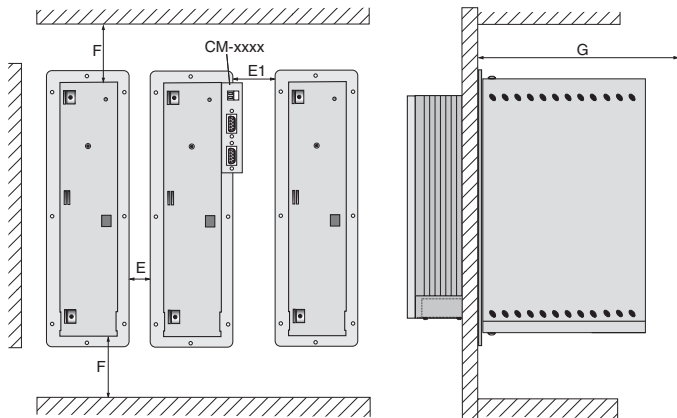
Espaces libres pour le montage (voir Tableau 2.4)
